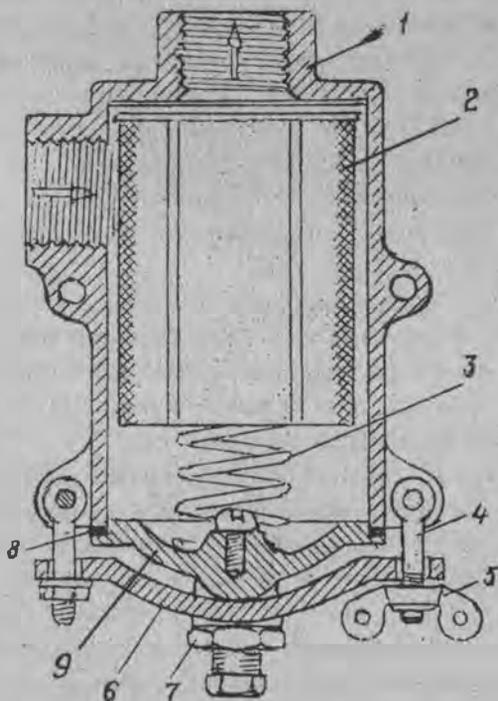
Фильтр грубой очистки топлива 811А-1 (фильтр-отстойник): 1 — корпус; 2 — фильтрующий элемент (сетка); 3 — пружина; 4 — ушковый болт; 5 — барашек; 6 — траверса; 7 — сливной кран; 8 — прокладка; 9 — крышка
